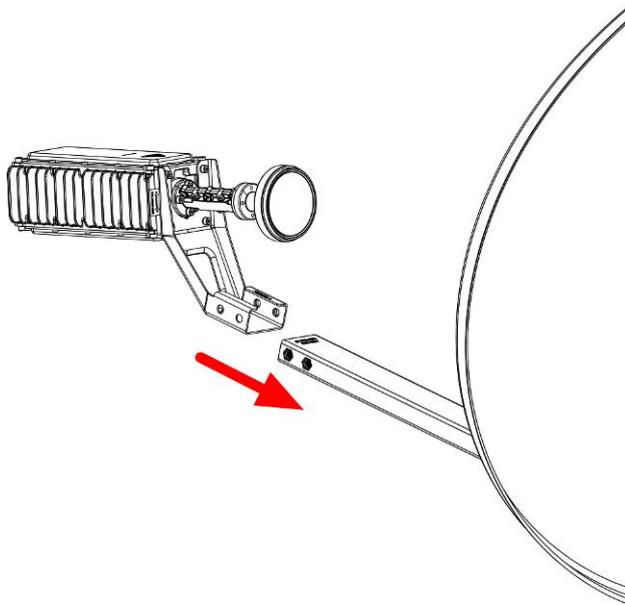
Сборка кронштейна приемопередатчика на штанге облучателя
